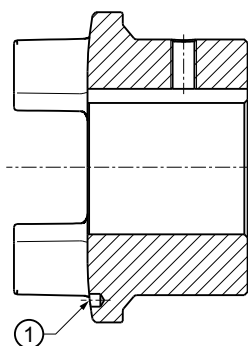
Position du trou d'équilibrage pour l'équilibrage à un plan
